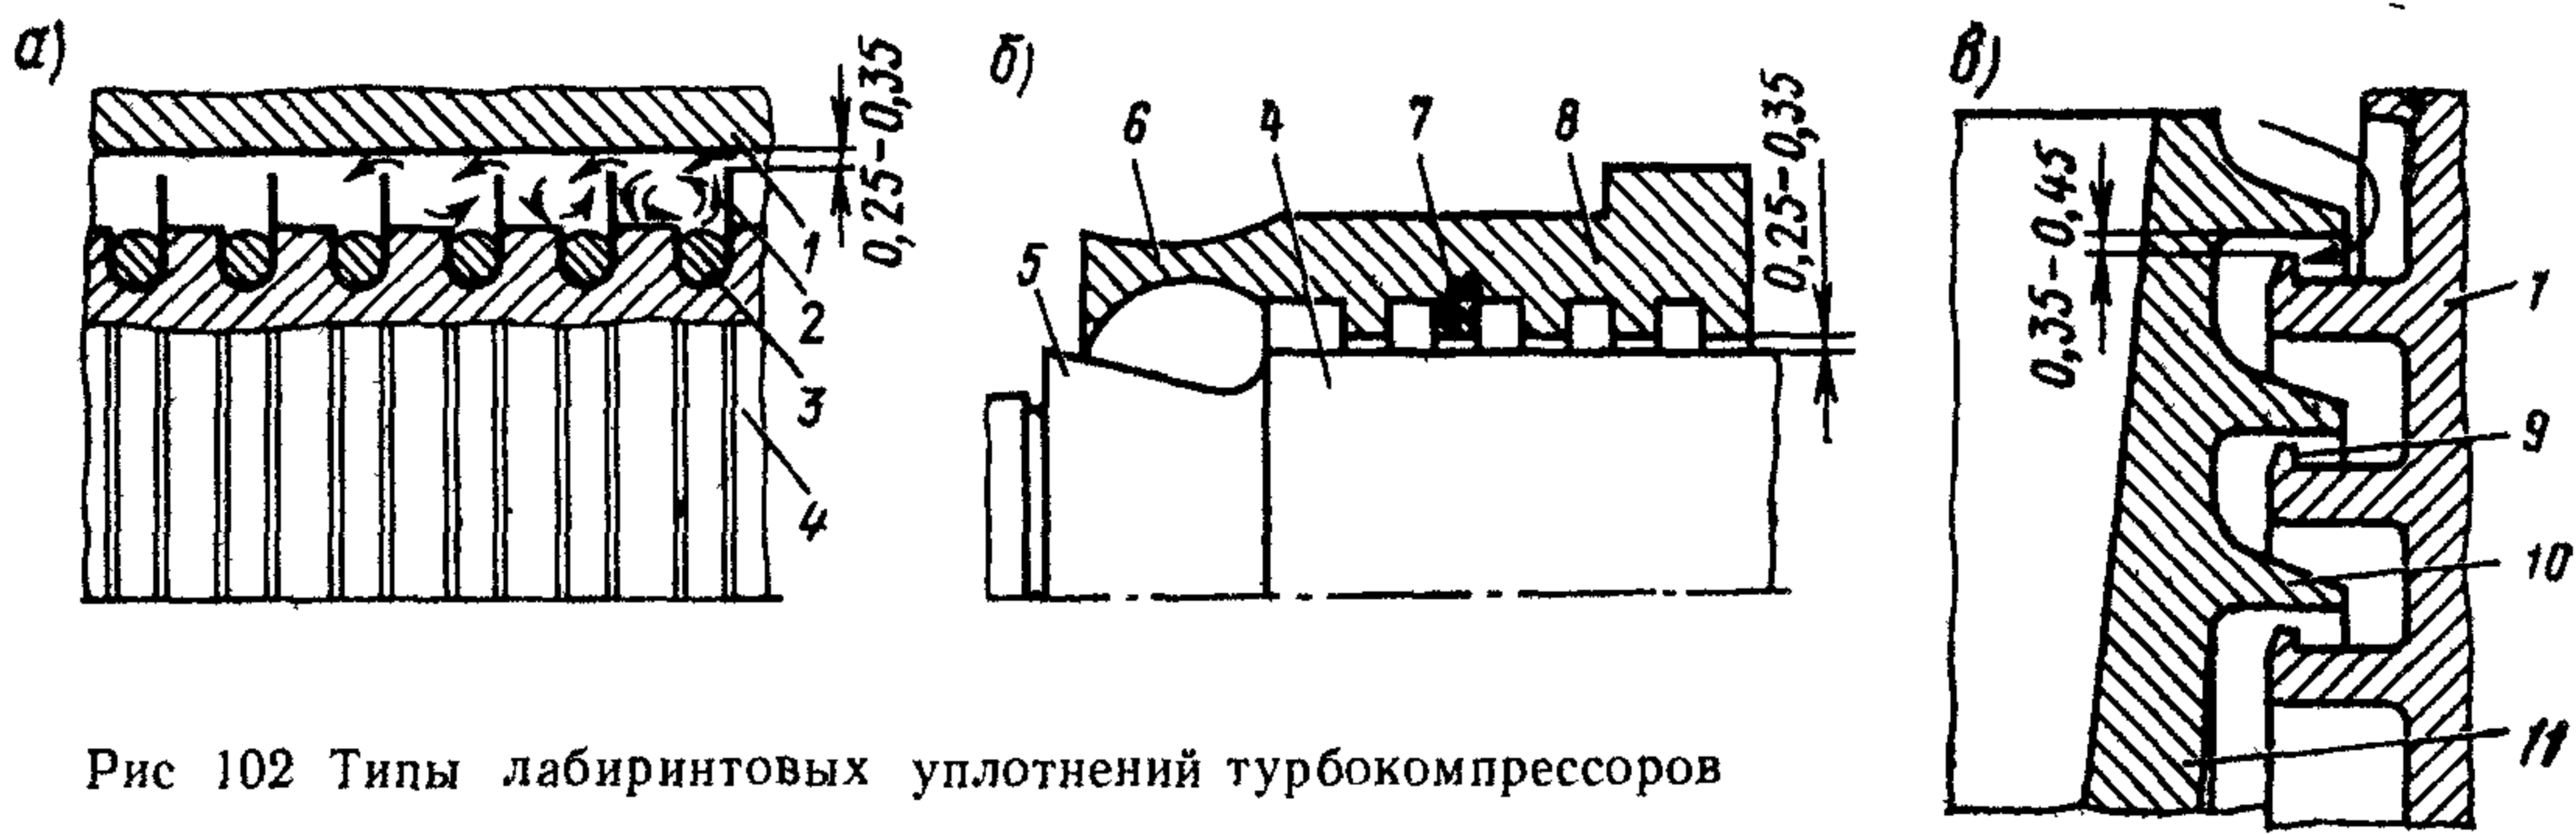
Типы лабиринтовых уплотнений турбокомпрессоров
